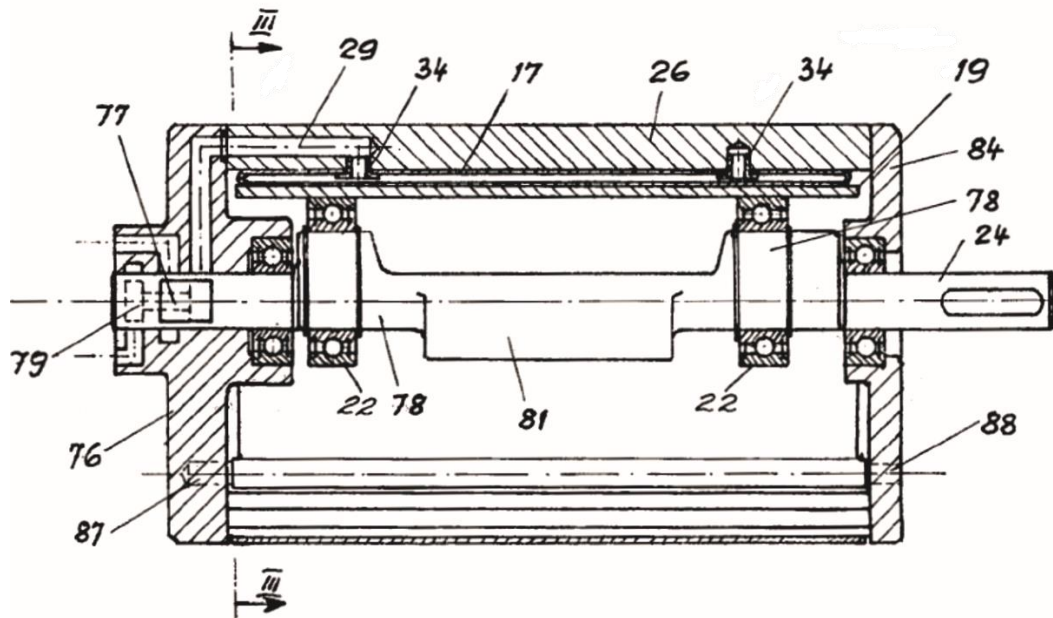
Konstrukce pneumotoru dle Patentu US3946641, typ bez desek, v řezu II-II z Obr. 4.7, převzato z [11]
